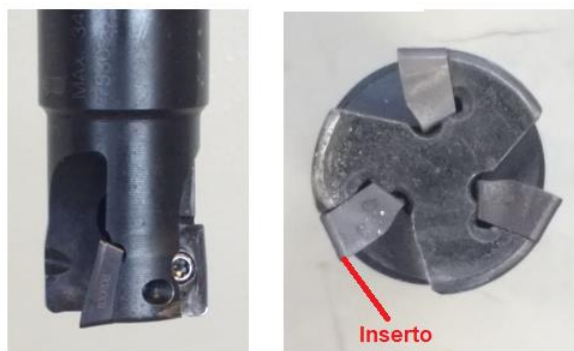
Ferramenta de usinagem (esquerda) e inserto (direita)
